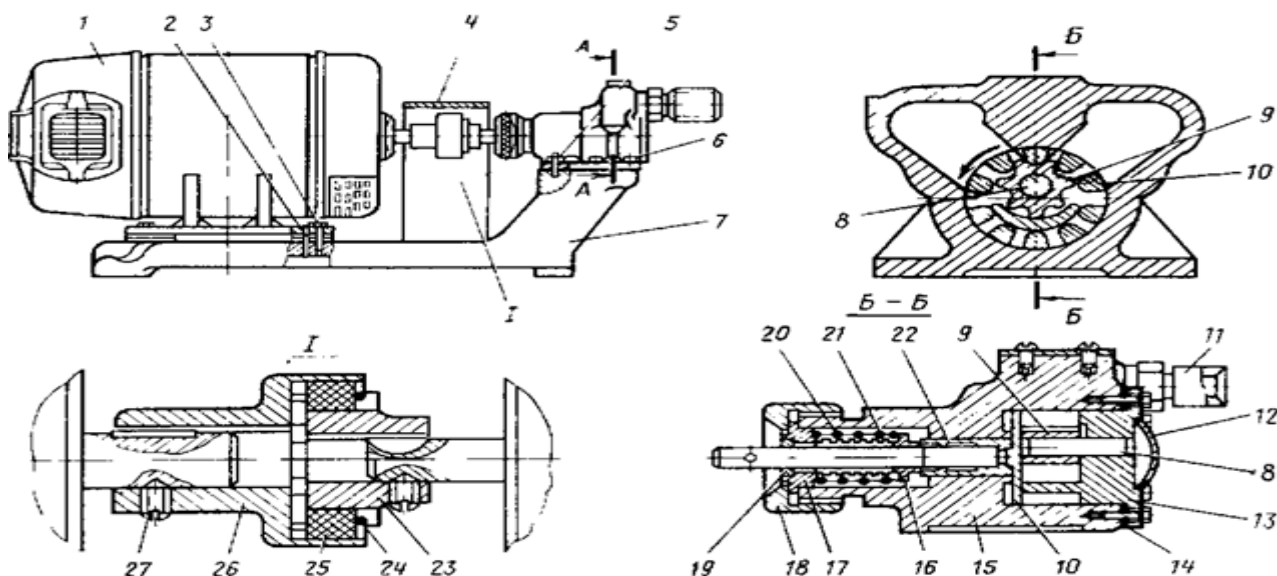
Топливоподкачивающий агрегат: 1-электродвигатель; 2, 5, 27-штифты; 3-шпилька; 4-кожух; 6-болт; 7-плита; 8-ось; 9- звездочка; 10-ведущая втулка; 11-штуцер; 12-заглушка; 13-крышка; 14-прокладка; 15-корпус насоса; 16, 19, 22-втулки; 17-уплотнительная втулка; 18-накидная гайка; 20-пружина сильфона; 21-сильфои; 23, 26-полумуфты; 24-стопорное кольцо; 25-палец резиновый
